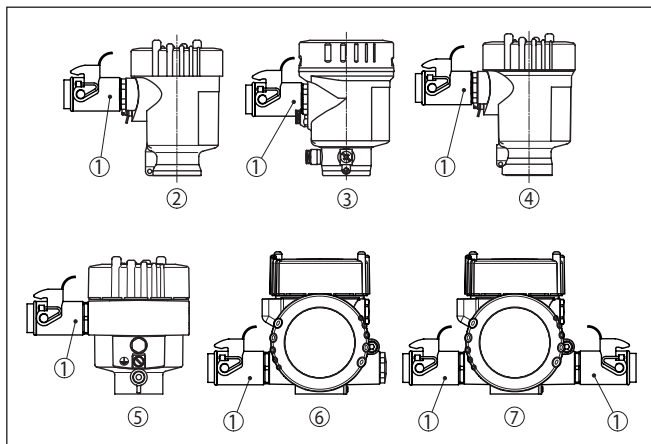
Положение штекерного разъема в разных исполнениях корпуса
